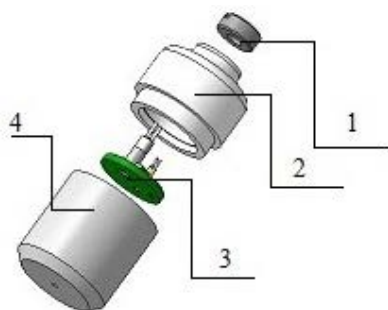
Внешний вид и компоновка оптического карандаша: 1 – гайка, 2 – корпус, 3 – плата, 4 – наконечник
